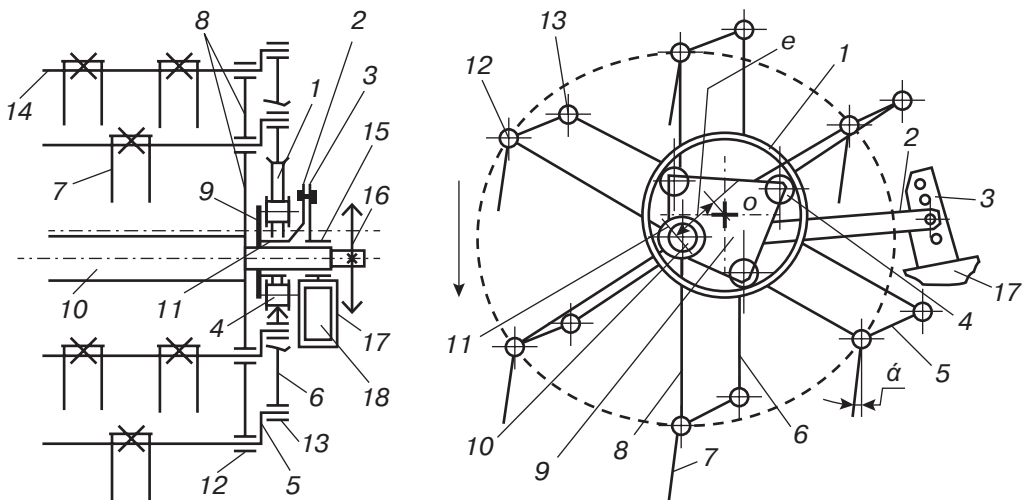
Принципова схема ексцентрикового мотовила:
